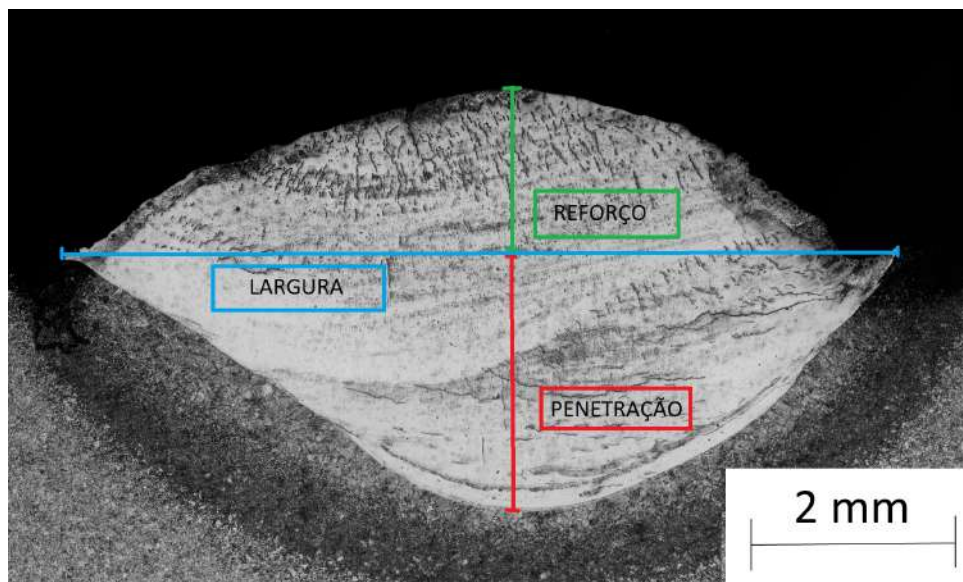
Medição do cordão de solda e do comprimento do eletrodo pós soldagem.
